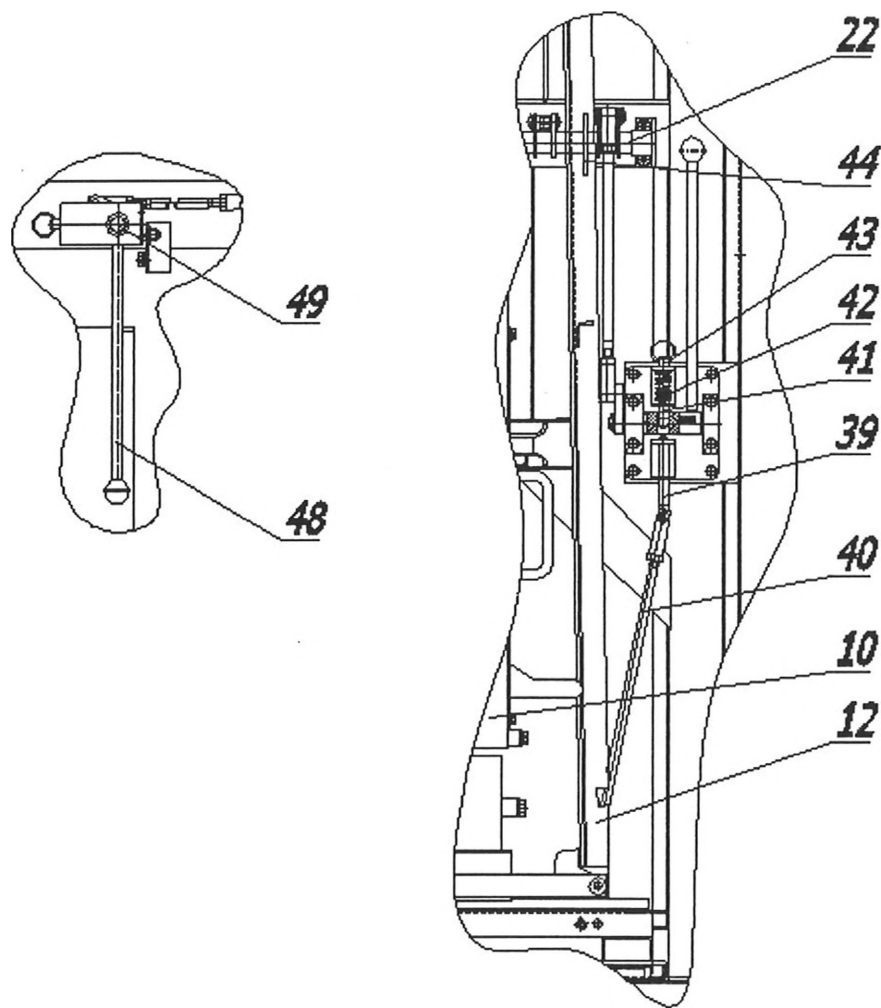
блокировка разъединителей и заземлителя с откидным рельсом 12
